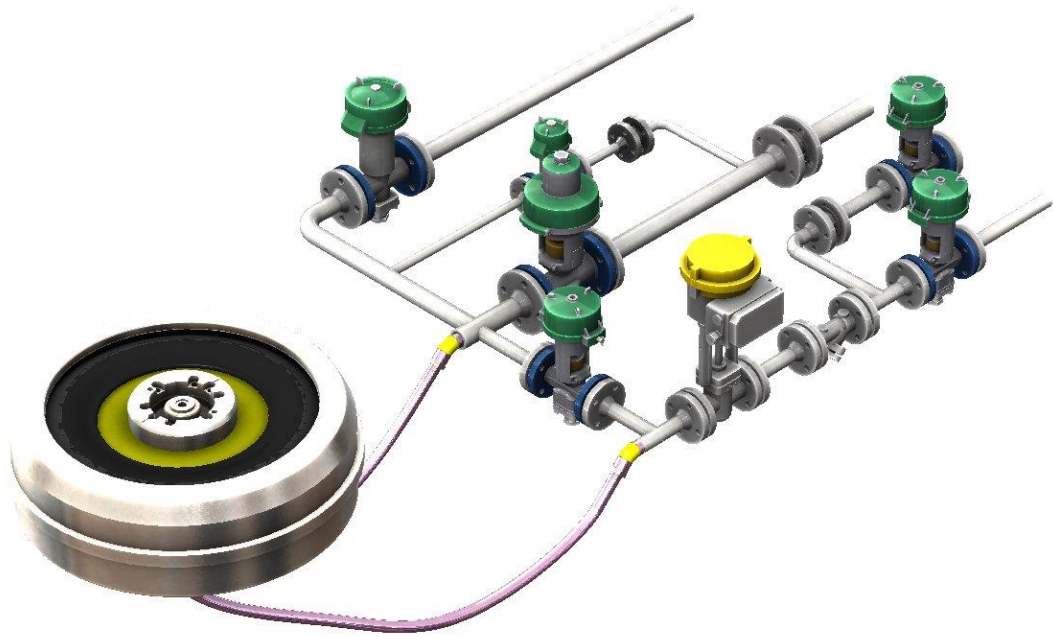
Conjunto de tubulação e molde, em vista isométrica.
